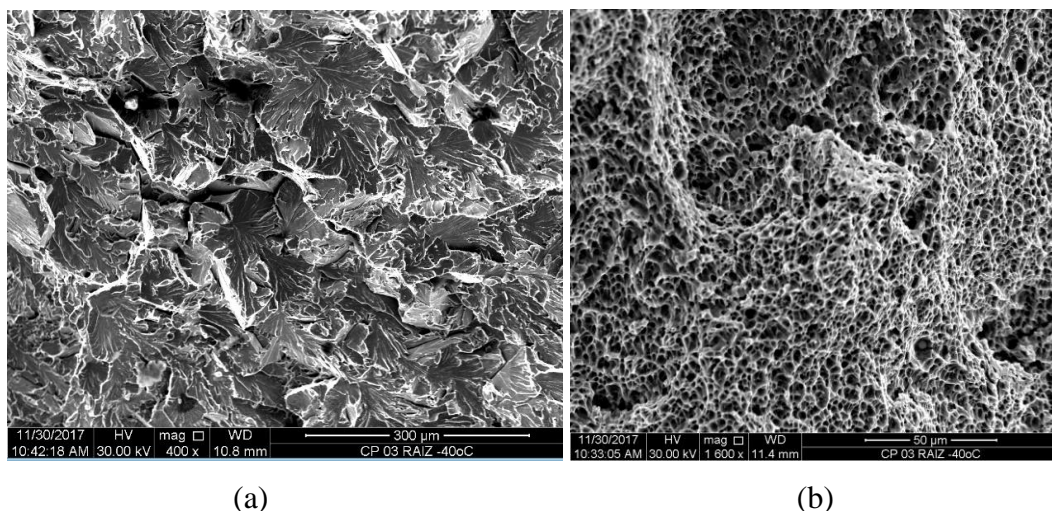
Superfície de fratura para o corpo de prova para condição APT-B com menor valor de energia à -40°C : (a) fratura frágil; (b) fratura dúctil
